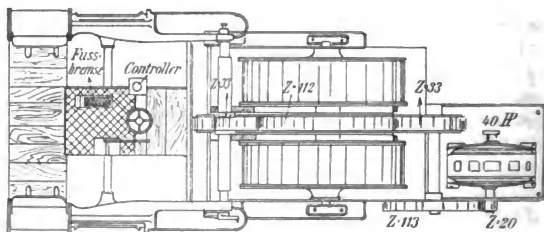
Fördermaschine mit kombiniertem Antrieb. Grundriss.
